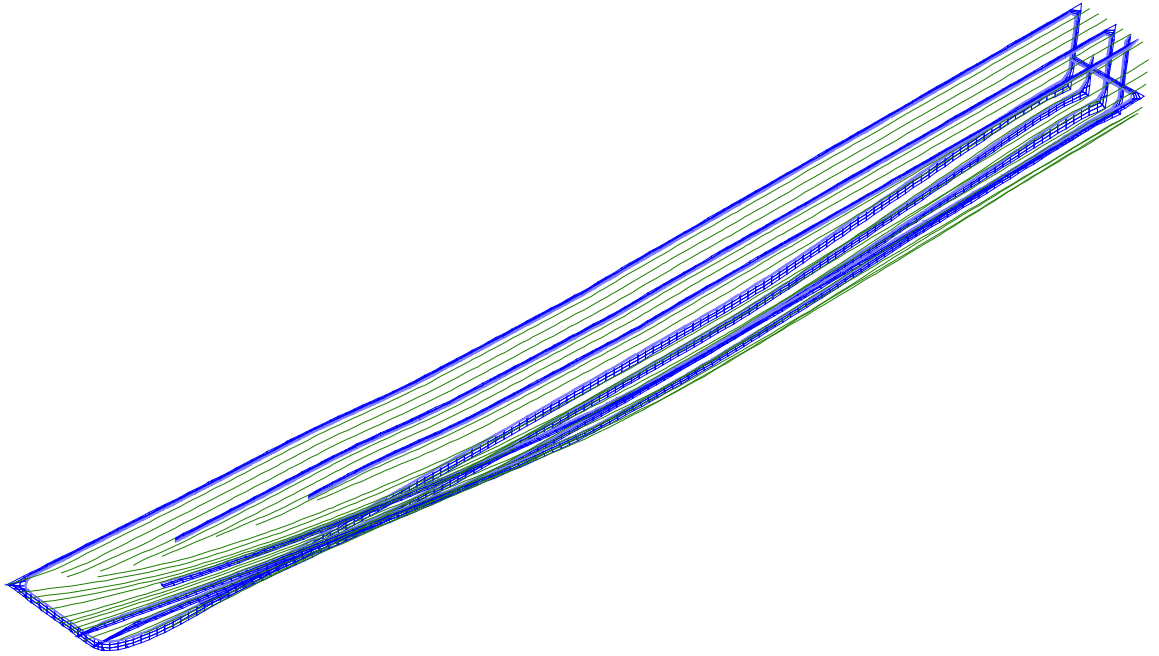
f: *Longitudinales de fondo, costado y cubierta (simples y reforzados)
